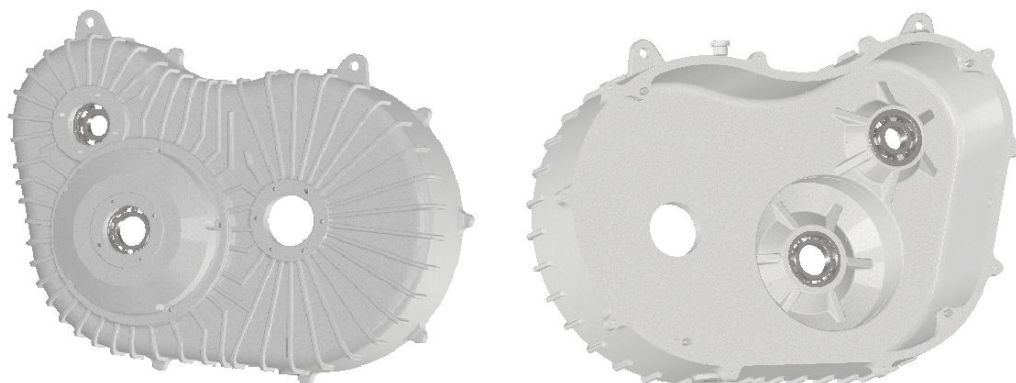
Montagem da tampa de embraiagem na metade esquerda do cárter e montagem dos rolamentos
